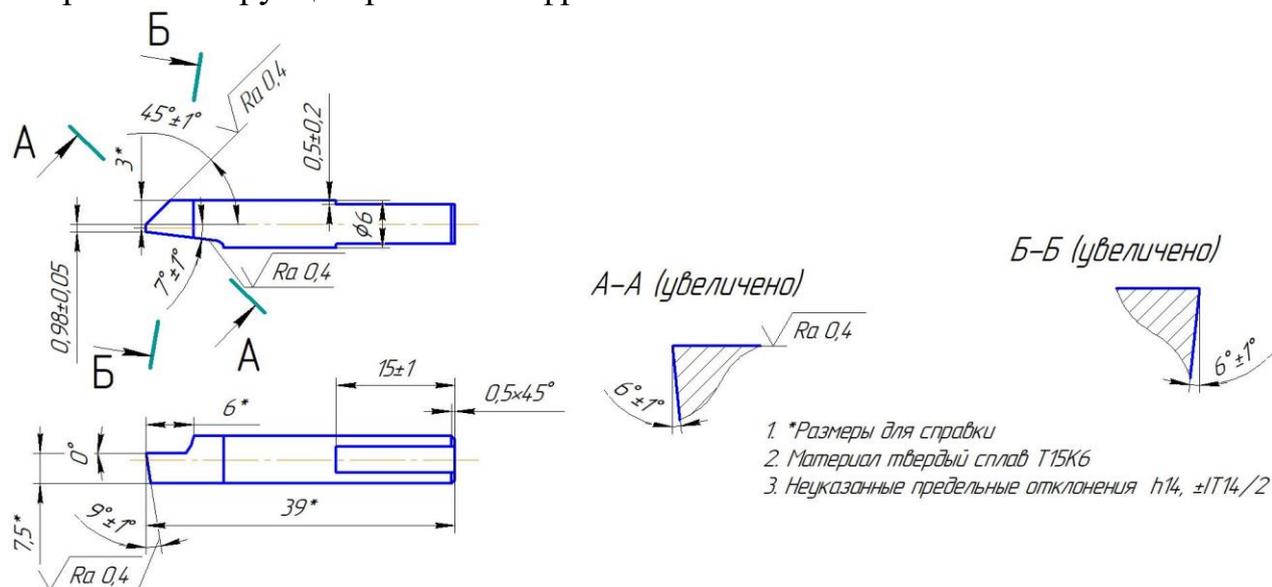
Рабочий чертеж резца с профилем упорной резьбы.
